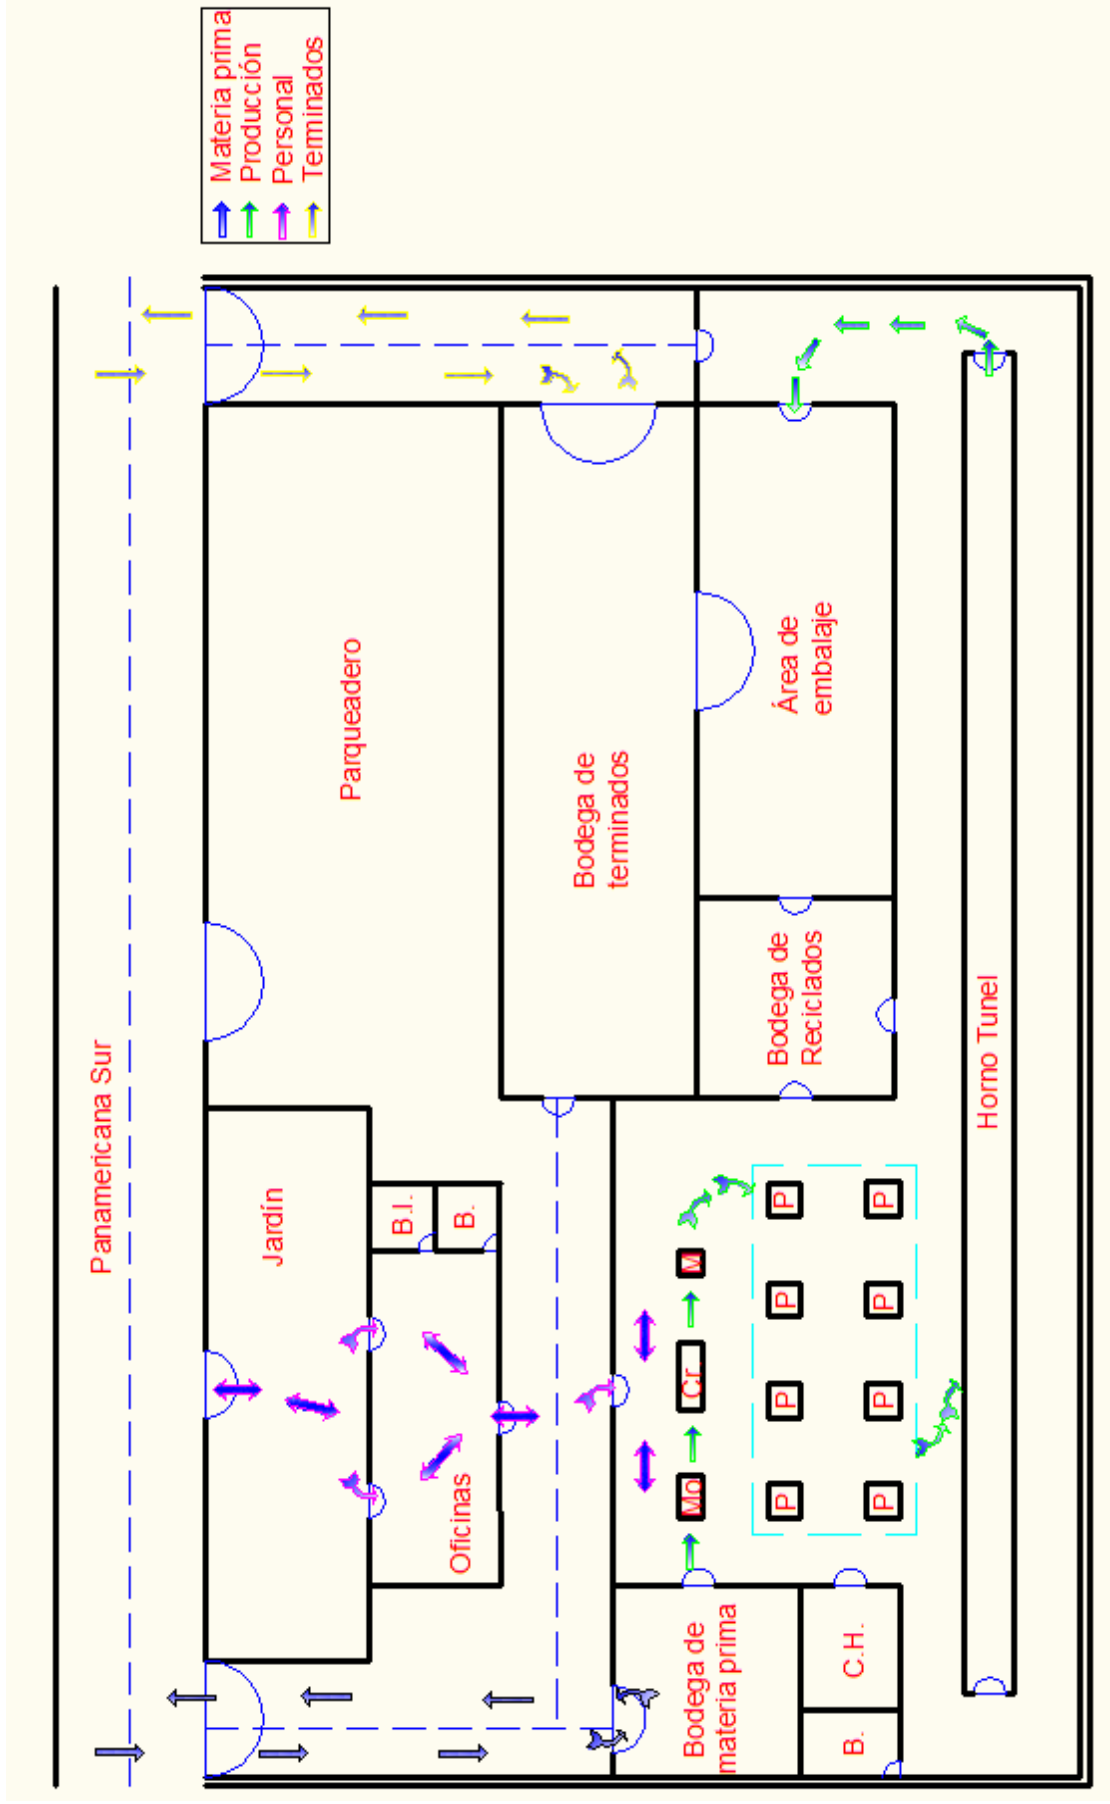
Distribución de planta con ingeniería especializada o de detalle (flujos)
